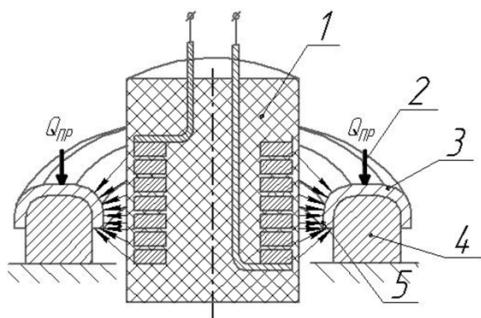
Схема обработки кольцевого образца давлением ИМП:
